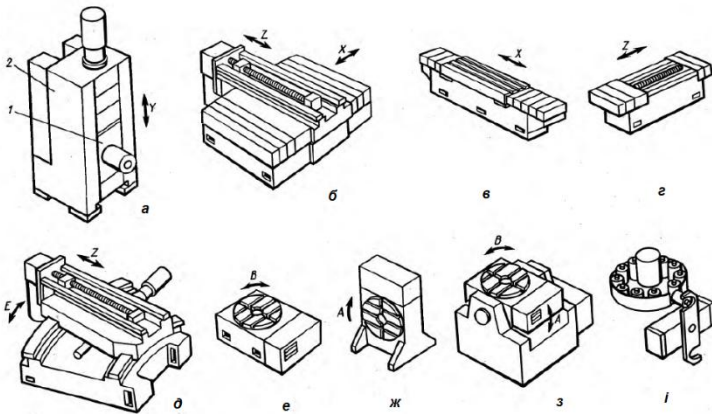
Уніфіковані елементи агрегатних верстатів з ЧПК
